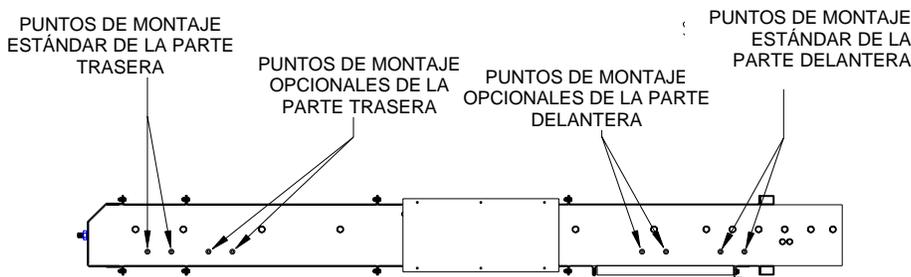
PUNTOS DE MONTAJE DEL ELEVADOR
